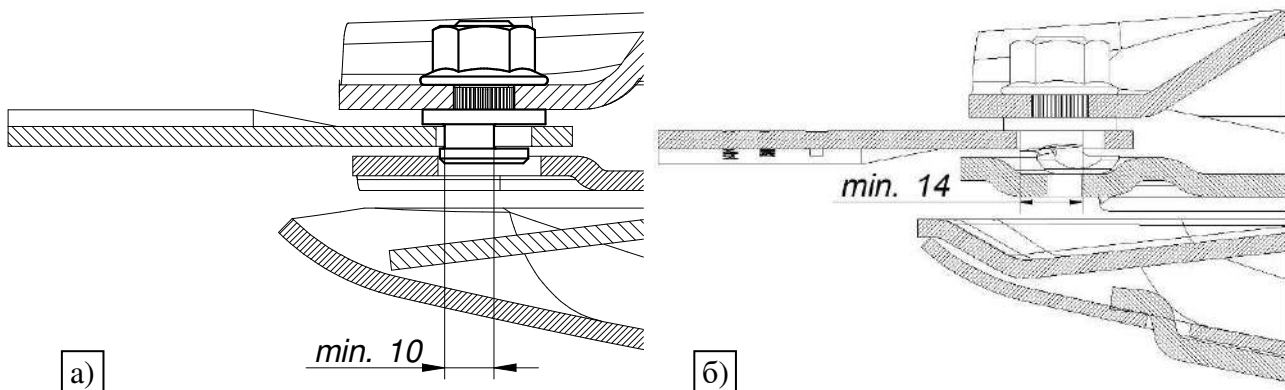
Допустимый износ стержня держателя ножей в диске а)ручка ножа М12
